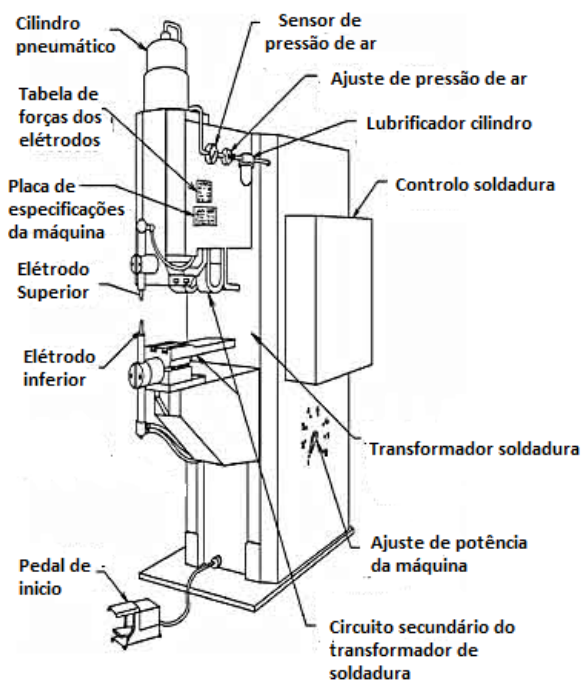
Elementos de uma máquina de soldadura pedestal
